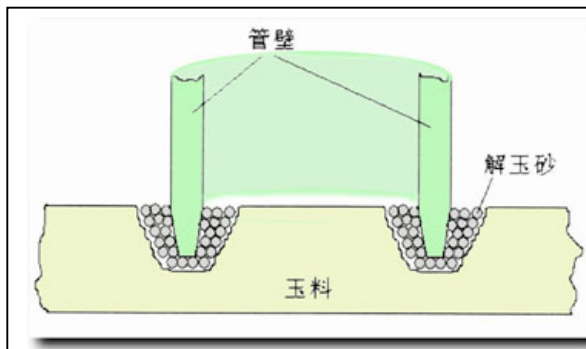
Ricostruzione della tecnica di trapanazione con trapano a punta cava.
